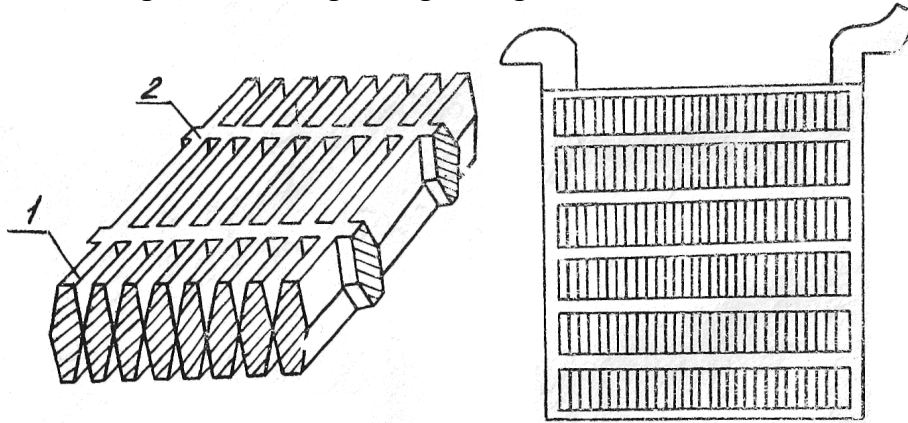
Поверхнева пластина із наскрізними ребрами та її розріз
